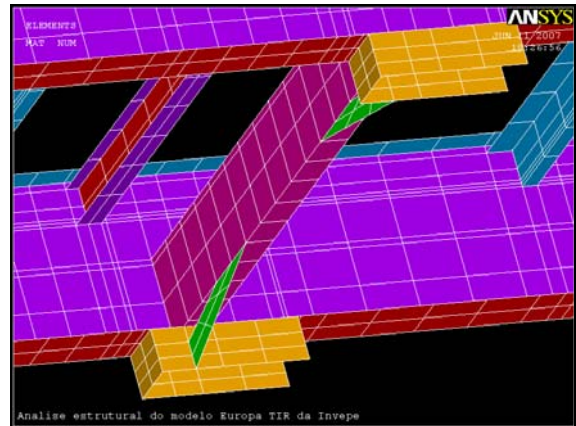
Pormenores da malha na zona de apoio do eixo e suspensão (escala mais apertada)
